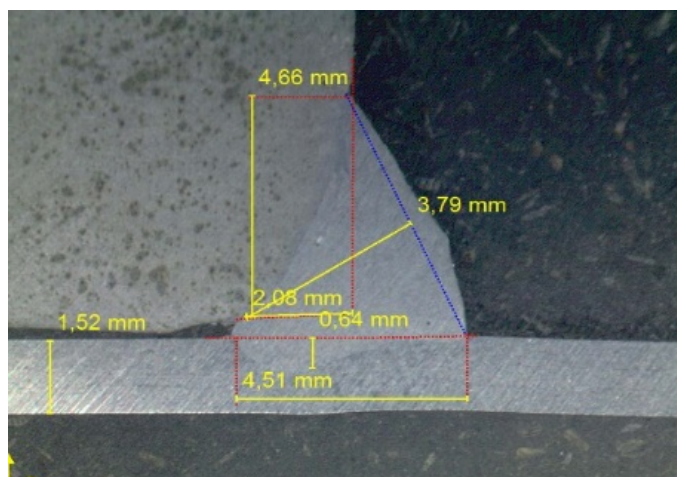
Exemplo da área solda entre o tubo e o flange de um dos conjuntos de testes estudados, bem como seus respectivos resultados de penetração de solda
